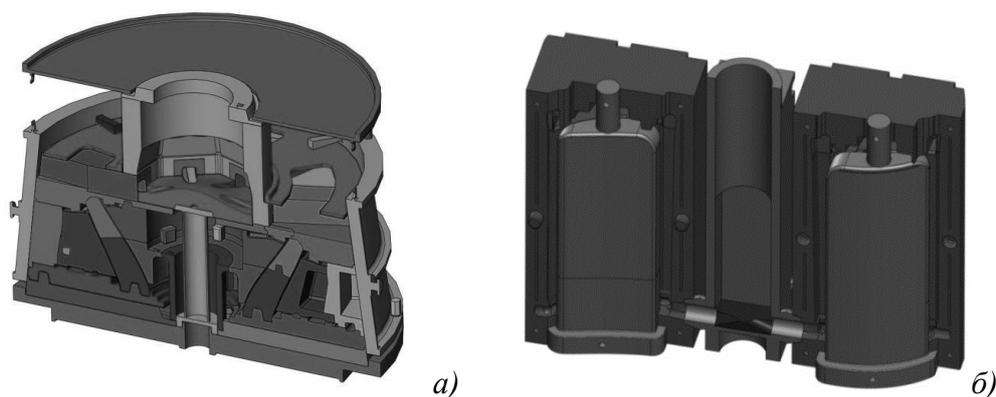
Вид литейной формы а) для отливки «Втулка» в разрезе (б) для отливки «Стойки» по плоскости разъема
